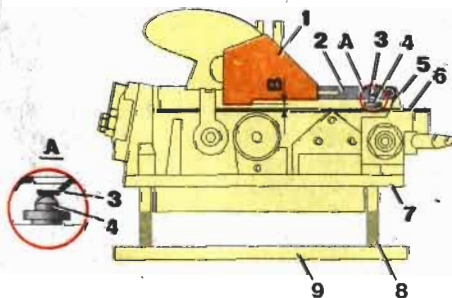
Схема регулировки уровня топлива: 1 - поплавок; 2 - кронштейн поплавков; 3 - язычок кронштейна; 4 - топливный клапан; 5 - ограничитель хода поплавков; 6 - прокладка крышки; 7 - крышка карбюратора; 8 - шпилька; 9 - поворачивающая плита; В - контролируемый размер
